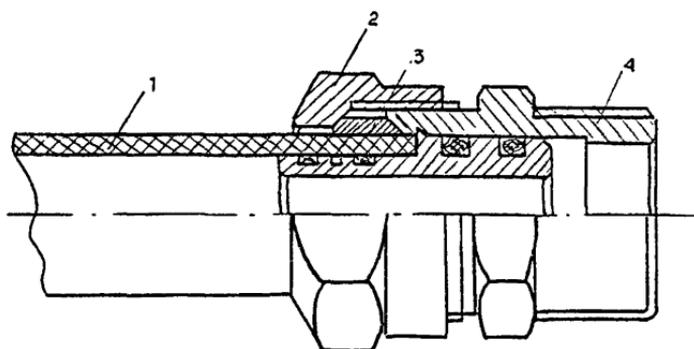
б. Соединение с накладной гайкой и разрезным кольцом:
